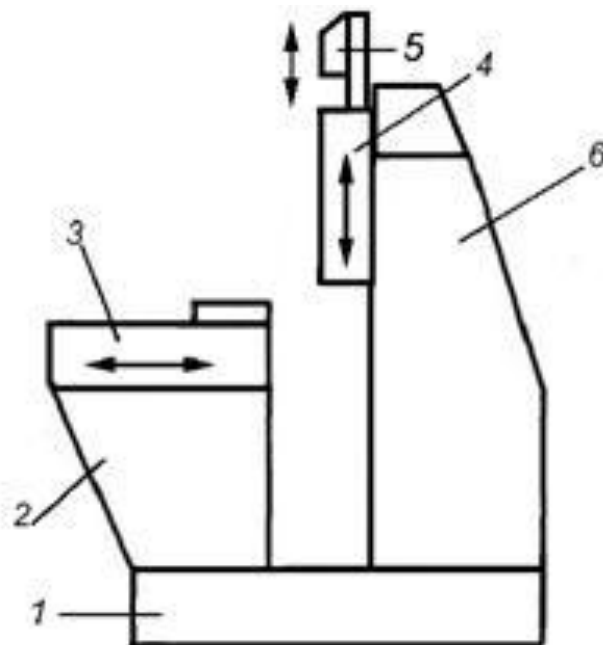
Схема компоновки вертикально-протяжного станка
